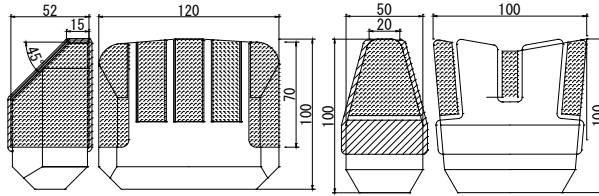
強化型(ビット 1) 図-3 先行(ビット 2) 写真-3 計測状況
